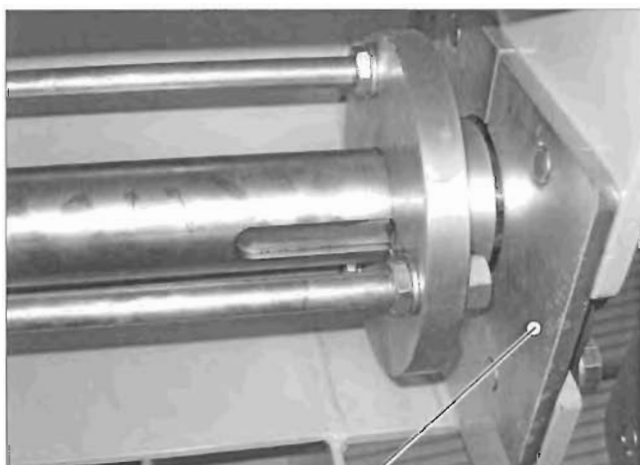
Внутренняя нижняя пластина на левом подшипнике фрезерного вала (неоснащенный вал)
